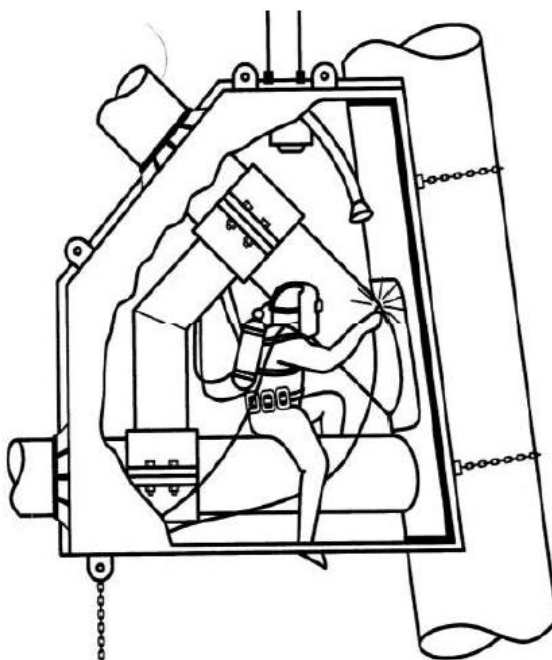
1: Soldagem subaquática seca em câmara hiperbárica.
